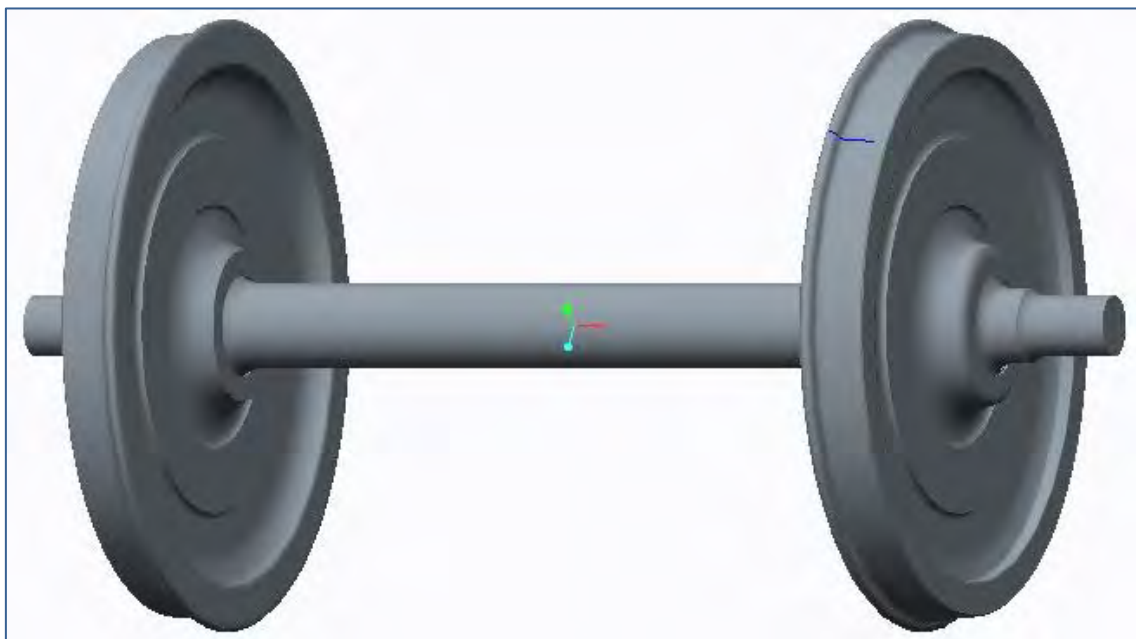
4. Situación de las piezas de conjunto, eje y ruedas
